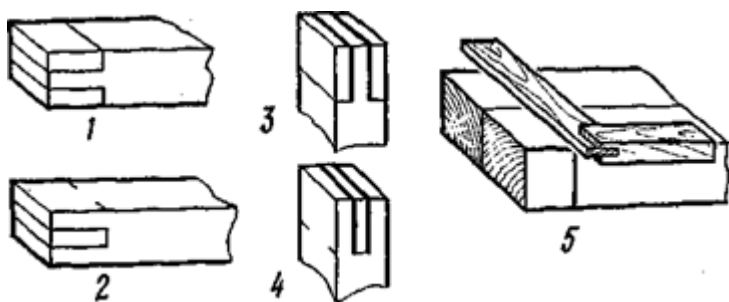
Разметка и образование шипов и проушин. Разметка угольником и рейсмусом: 1 — шипа; 2 — проушины; зашлифовывание: 3 — шипа; 4 — проушины; 5 — разметка двух брусков угольником
